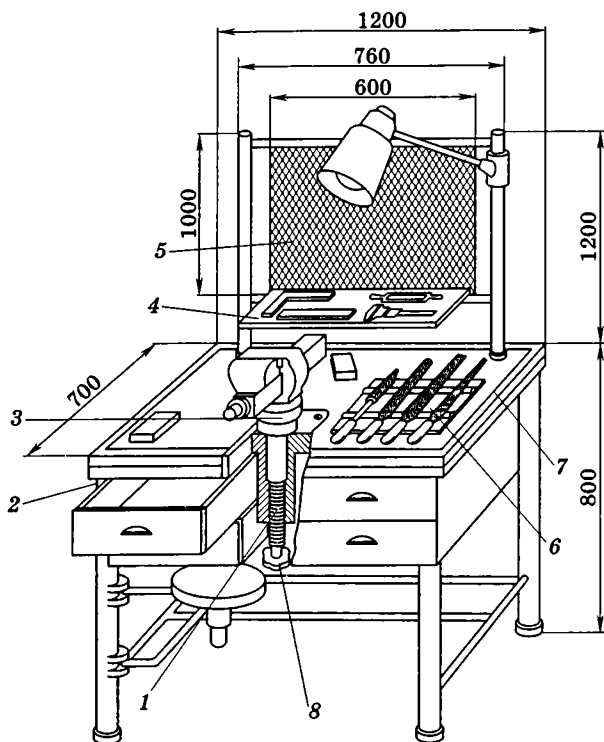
Слесарный верстак с регулируемыми по высоте тисками: 1 — регулирующий винт; 2 — каркас; 3 — хвостовик тисков; 4 — полочка для измерительного инструмента; 5 — защитный экран; 6 — планшет для рабочего инструмента; 7 — планки-бортики; 8 — маховичок
